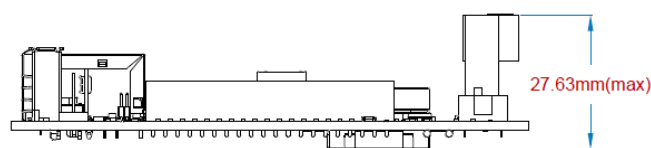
Dimensões mecânicas CPU LPC17 (PR17032)
